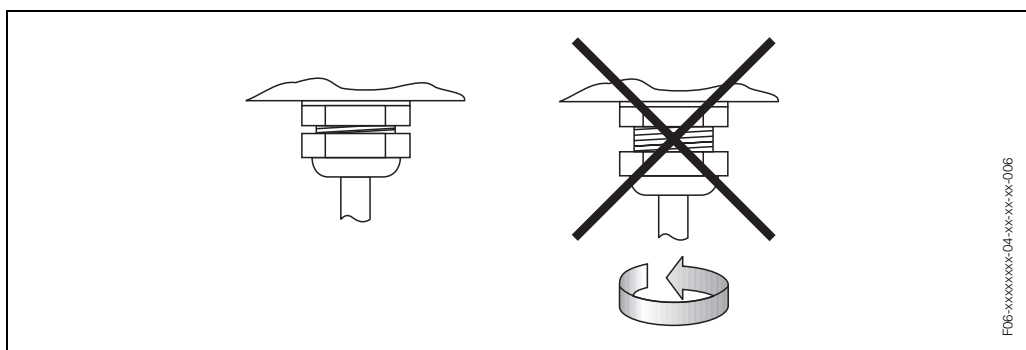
Instrucciones de instalación referentes a las entradas de cables en la caja del transmisor
